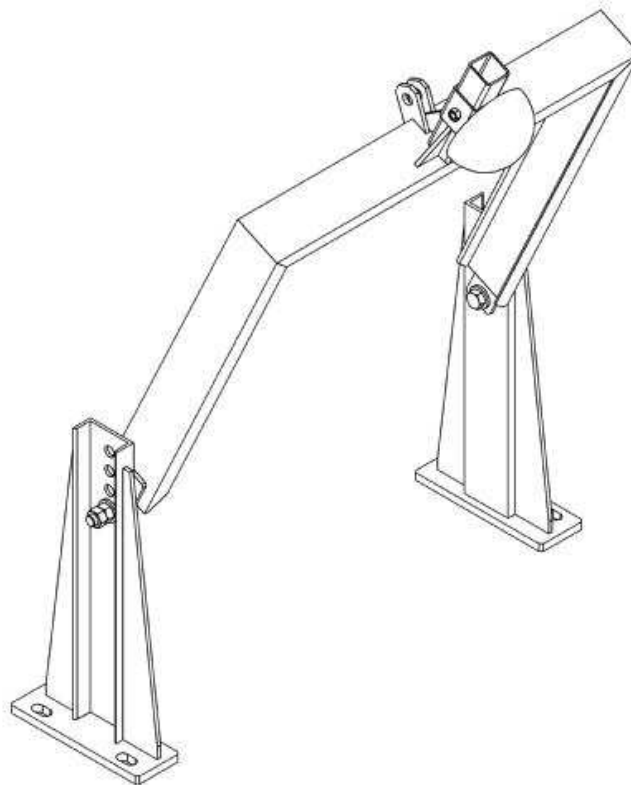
Dispositivo para ensaio do apoio de cabeça - Ensaio estático
